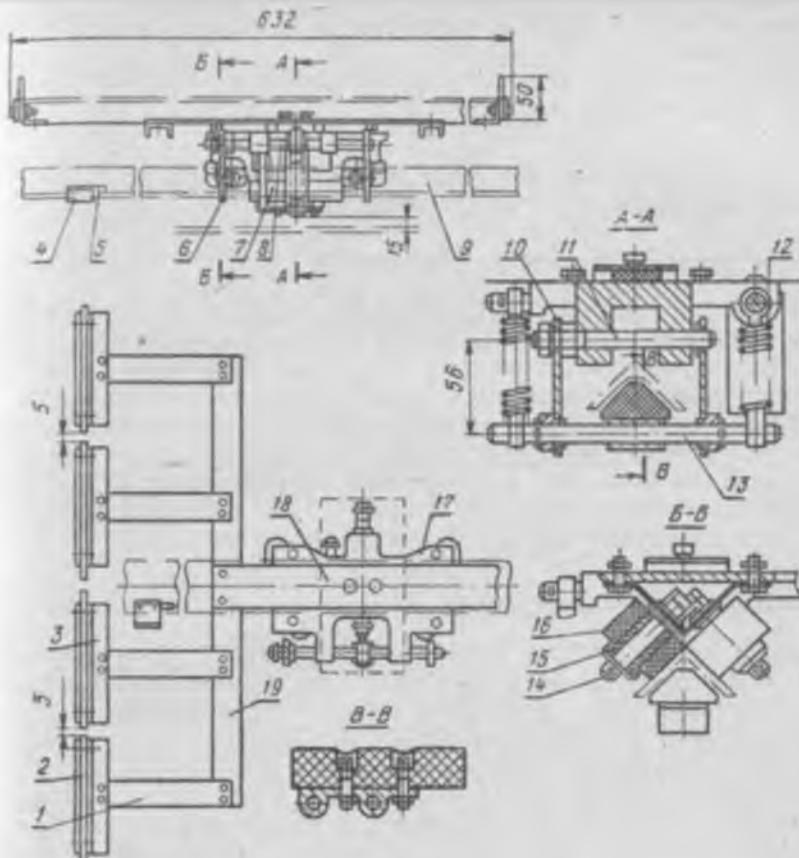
Инерционный очистительный механизм НУ-65М2:
